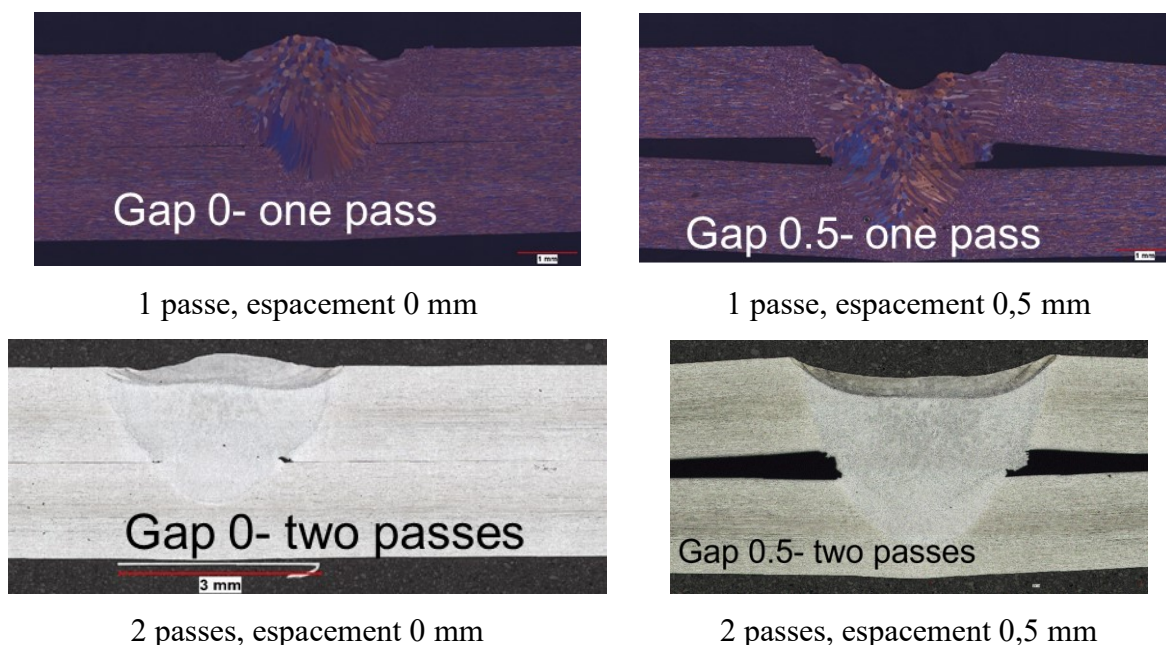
Coupes du trait de soudure des joints soudés
